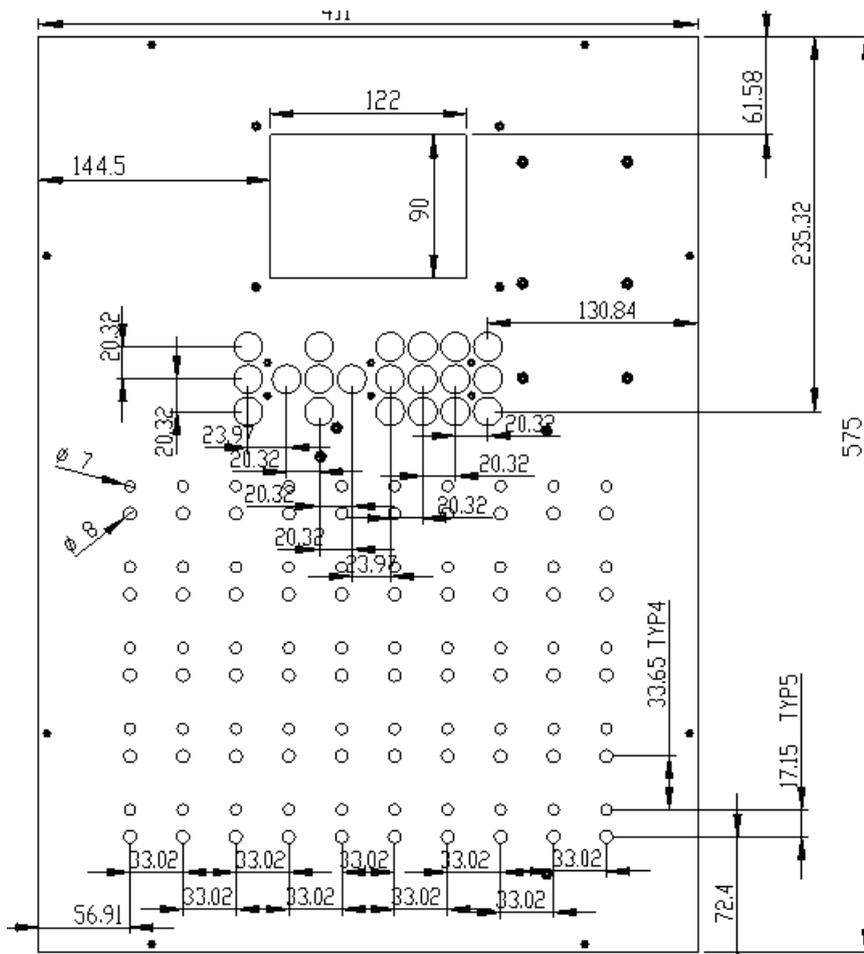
Platinum Pro 50 Dimensões do Painel Frontal
